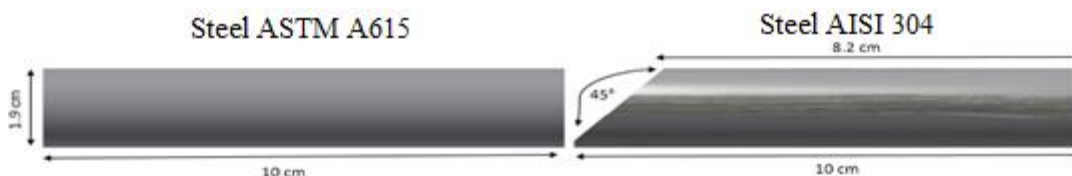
Diagrama de uma junta soldada com um único bisel a 45°.
